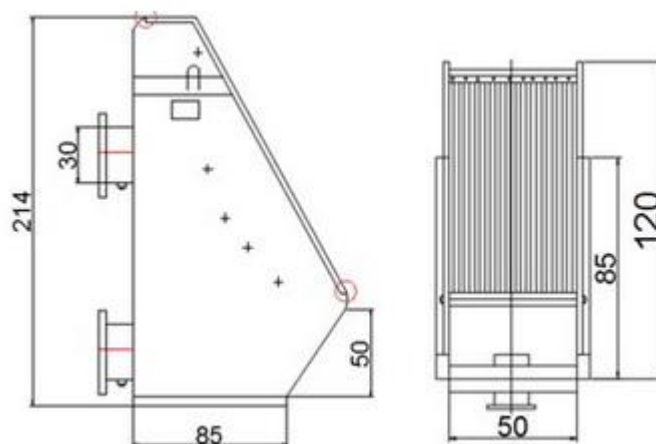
Dimensões da peneira estática (vista lateral e planta baixa, respectivamente).
